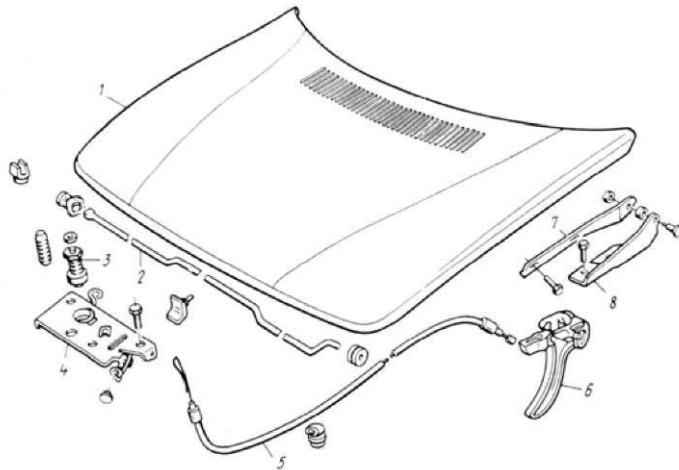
Капот двигателя автомобиля с механизмом открывания: 1 -капот; 2 -тяга; 3 -отпирающий палец; 4 -замок; 5 -трос капота; 6 -рукоятка открывания капота; 7 и 8 -шарниры
